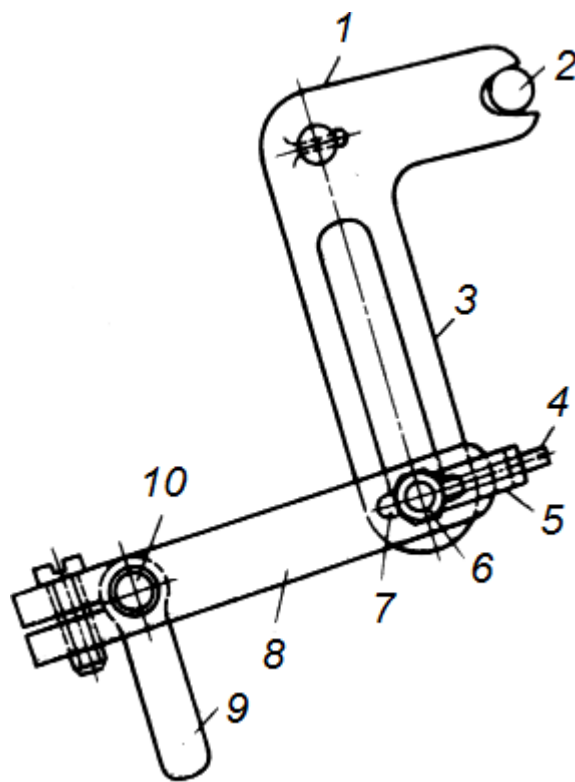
Конструктивна схема пристрою опускання голочниці.
